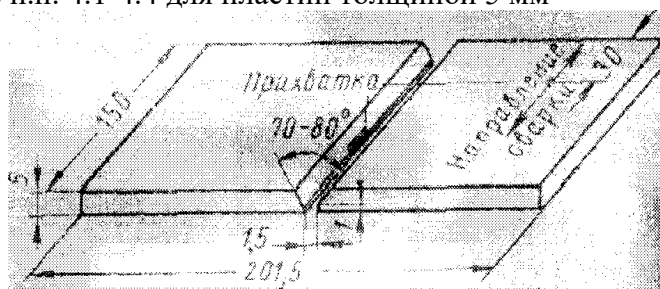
Схема сборки пластин из нержавеющей стали толщиной 5 мм
